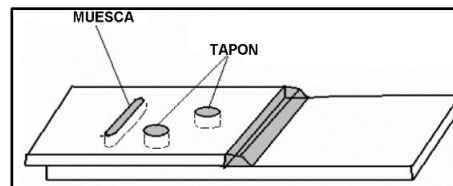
Detalle de soldadura tipo ranura. Fundacion Tecnologica Antonio de Arevalo (2018)
